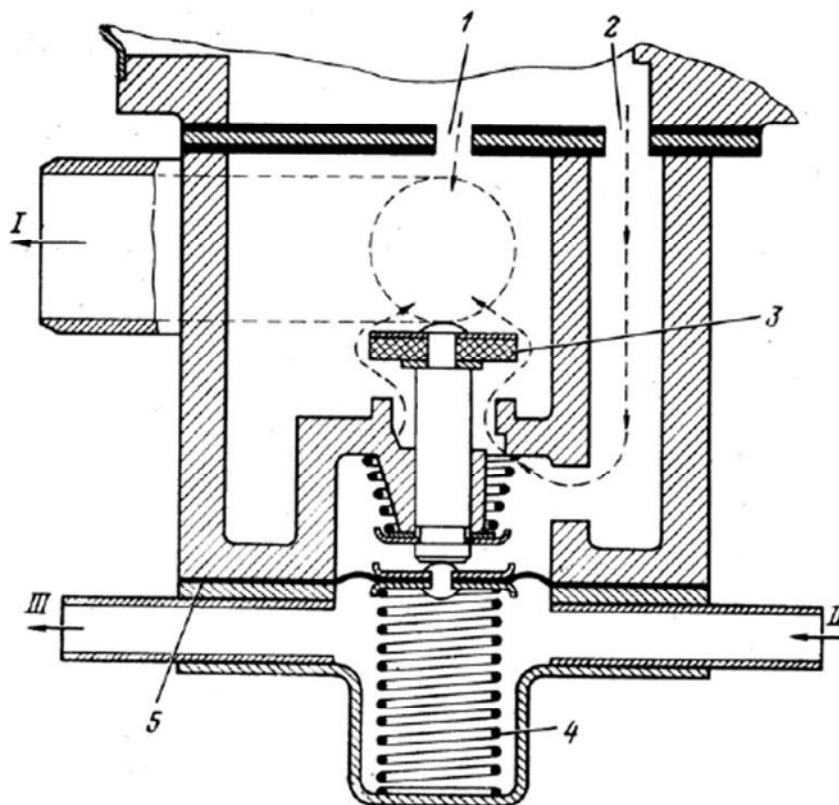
Дозирующе-экономайзерное устройство: I - выход газа к смесителю; II - вход от впускного трубопровода; III - выход к разгрузочному устройству; 1 - отверстие экономической подачи топлива; 2 - отверстие мощной регулировки подачи топлива; 3 - клапан дозирующе-экономайзерного устройства; 4 – пружина; 5 - диафрагма экономайзерного устройства
